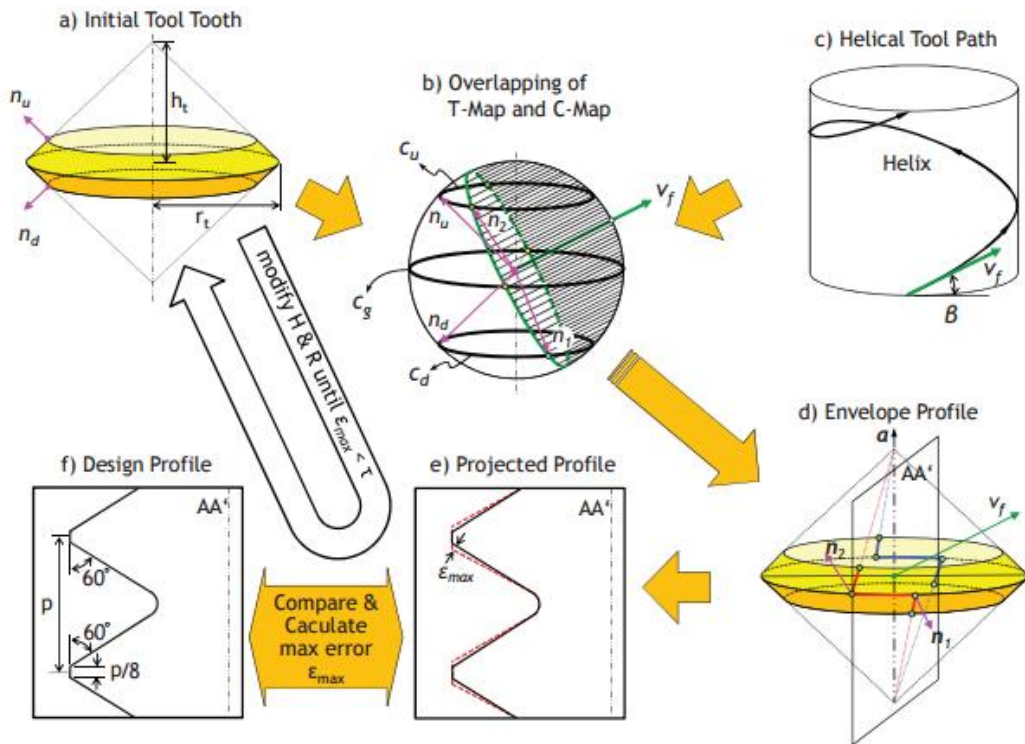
Схема послідовності методу формування дійсного профілю робочої поверхні різьбової фрези [15]
